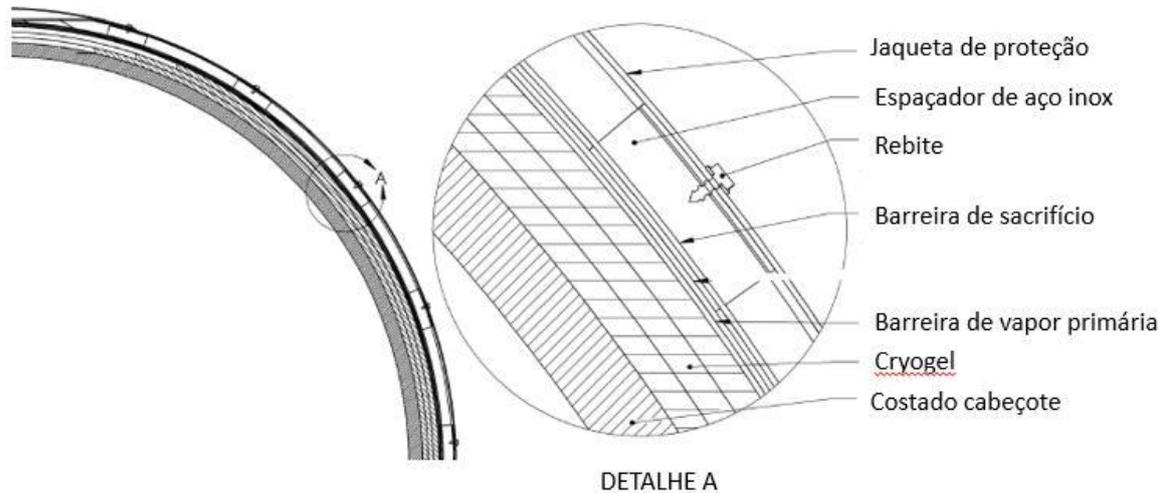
Detalhe para aplicação da jaqueta de proteção.
